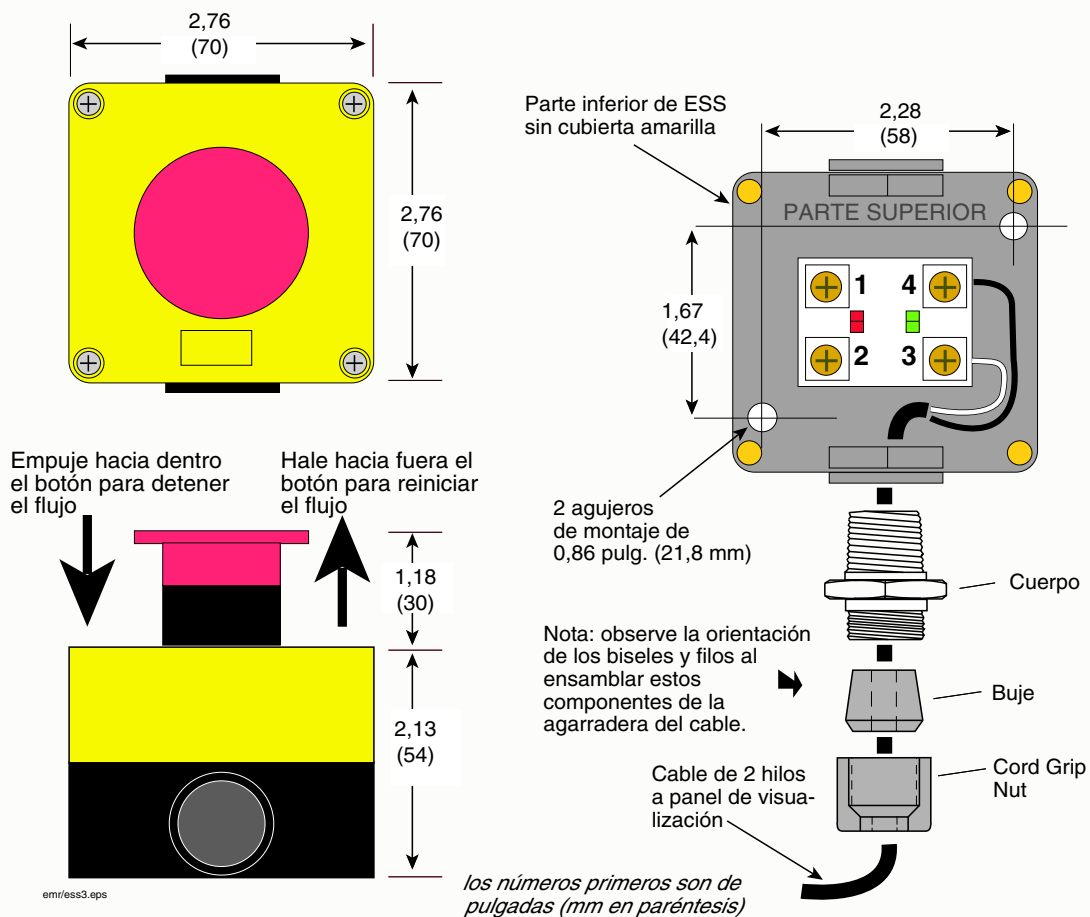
Montaje del interruptor de parada de emergencia y diagrama de cableado
